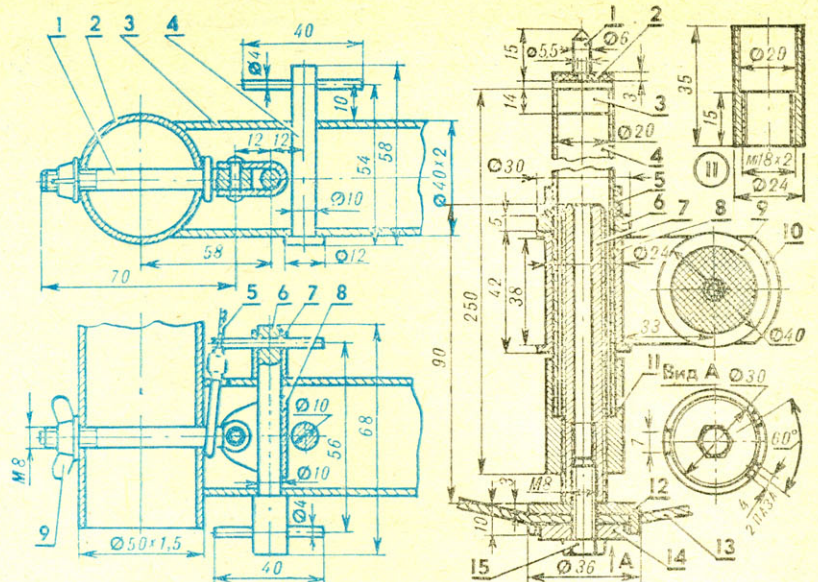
Типовой носовой (кормовой) соединительный узел стрингера и поперечной балки:
